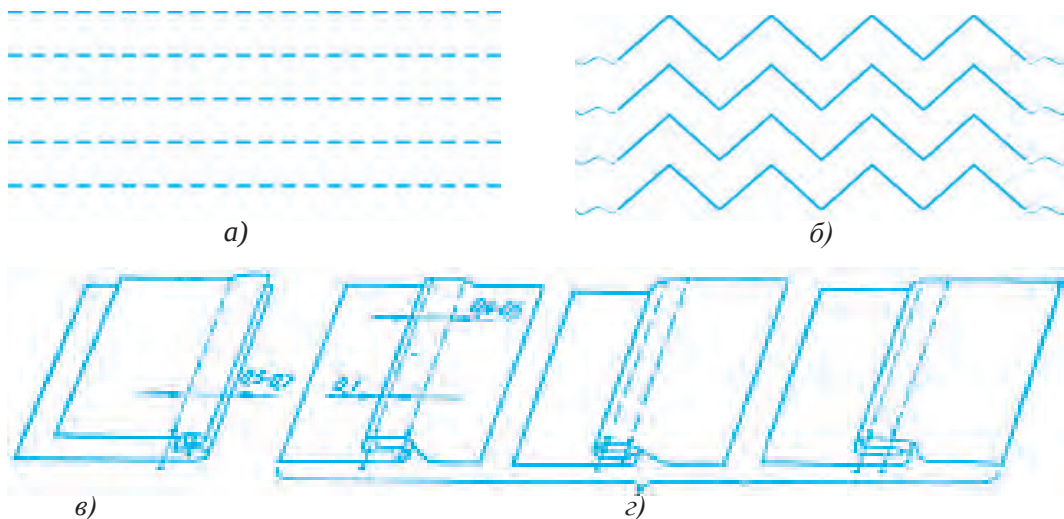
Образцы строчек и бельевых швов: а – параллельные строчки; б – зигзаг строчки; в – двойной шов; г – запошивочный (бельевой) шов.
